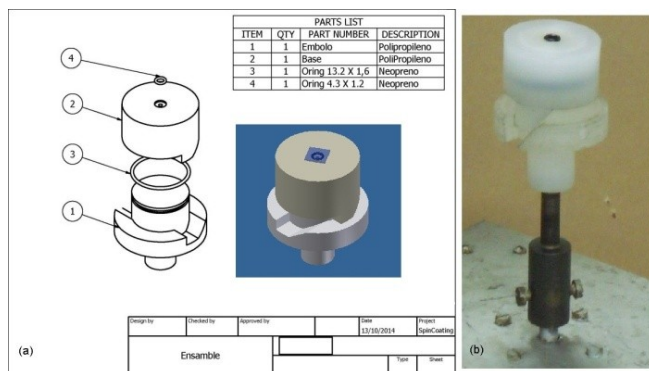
Conjunto camisa - émbolo. Plano (a) y foto (b).
